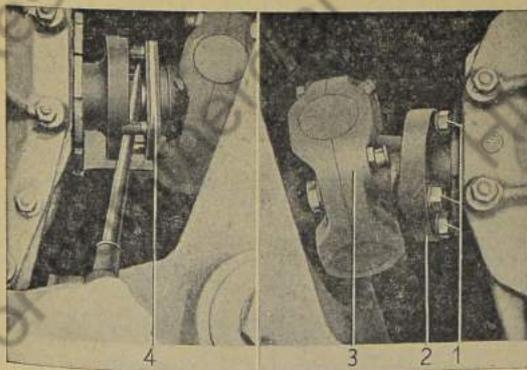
Quergelenkwelle von der Flanschwelle abschrauben
